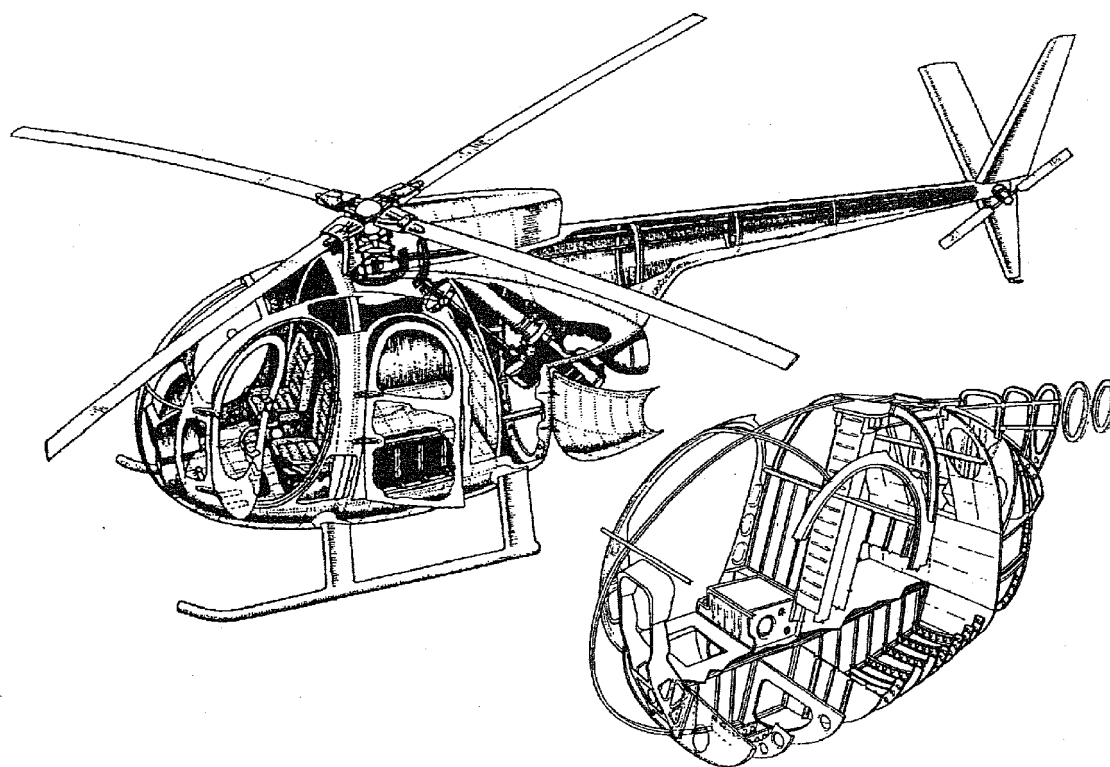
Конструкция фюзеляжа вертолета одновинтовой схемы MD-500
